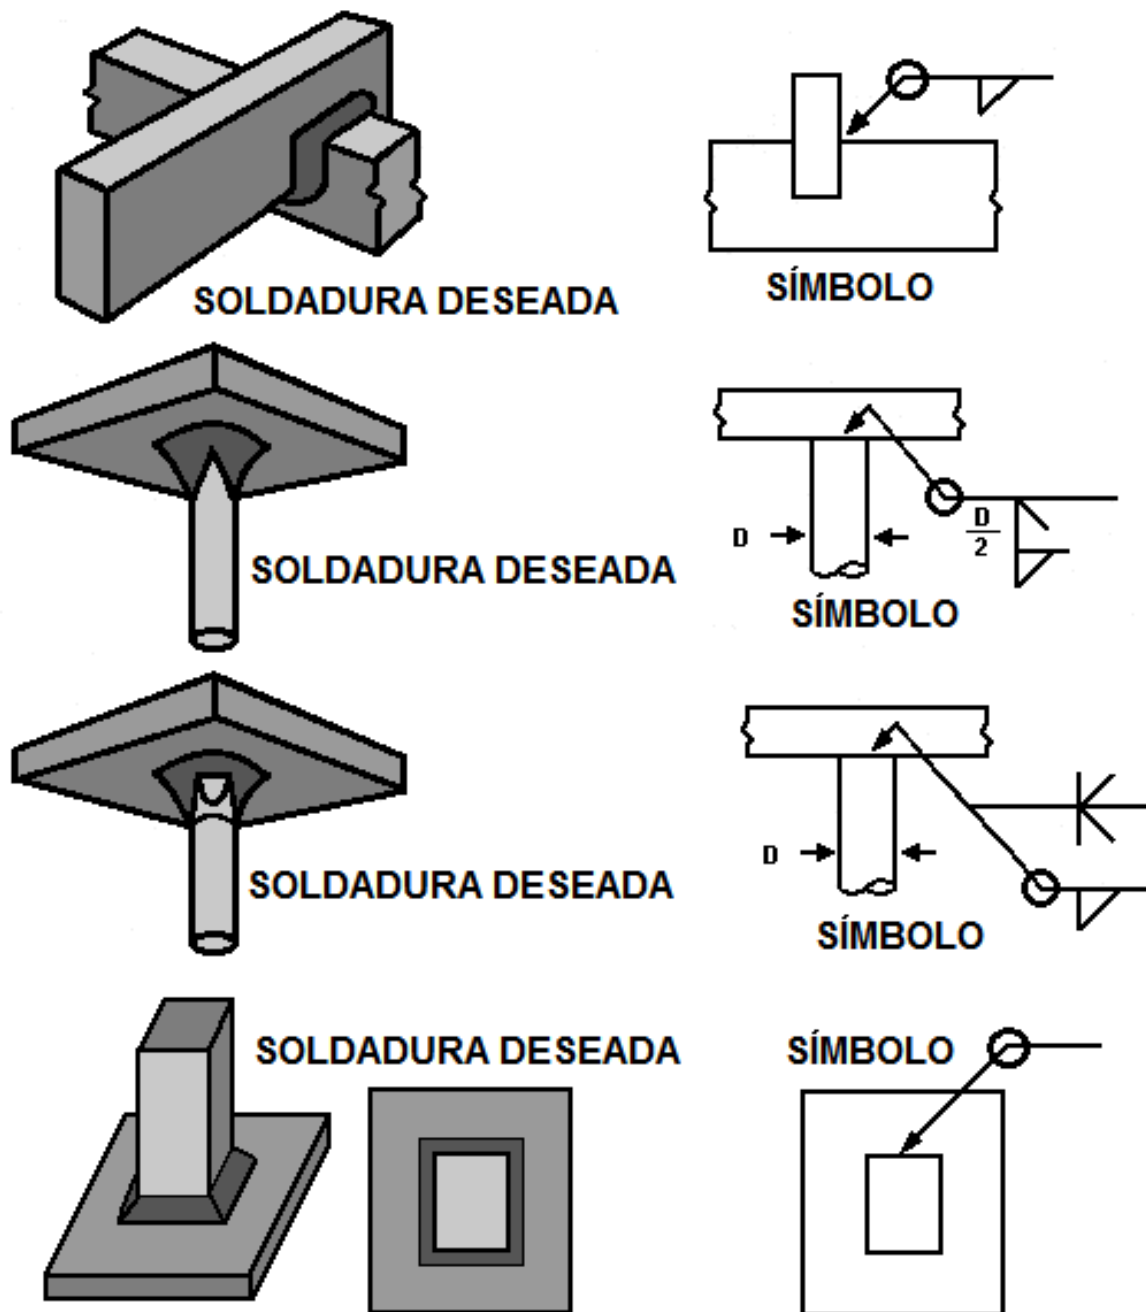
Dimensiones y forma de la soldadura en contorno (8, 18, 31)
